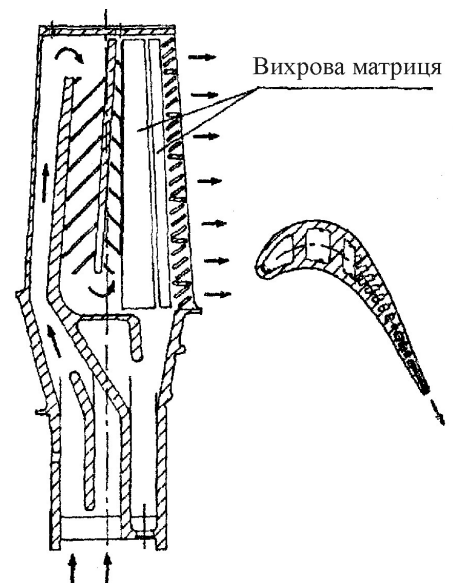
Конструкція охолоджуваної робочої лопатки з вихровою матрицею
